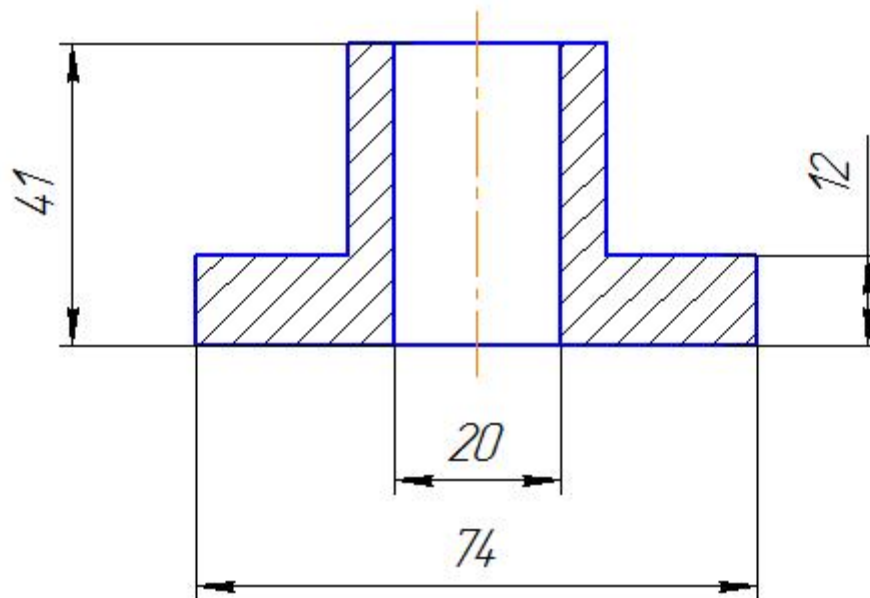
Заготовка для виготовлення деталі "Фланець"
